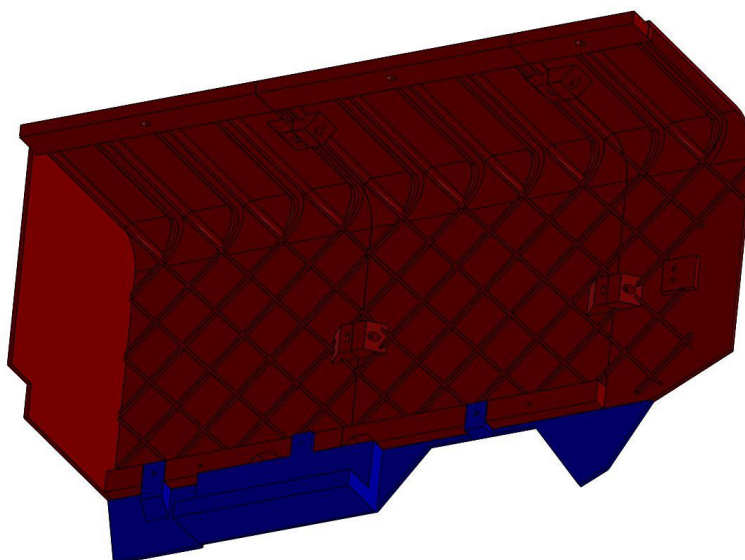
Finální verze sestavy kabiny [archiv autora]
